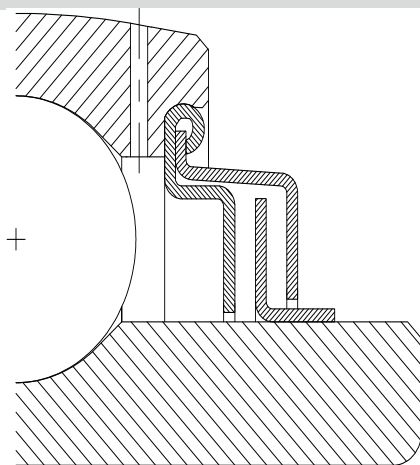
уплотнение типа L для корпусных подшипников NKE
